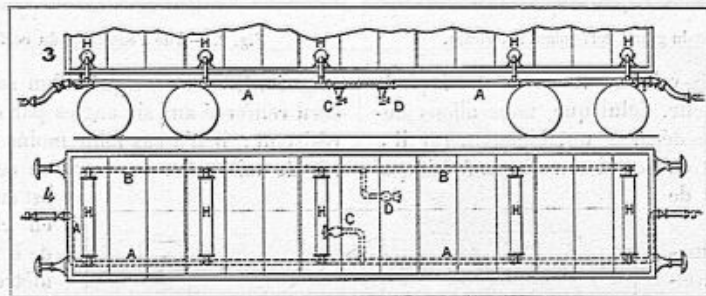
et 4. — Disposition de l'appareil. — Coupe et plan.
